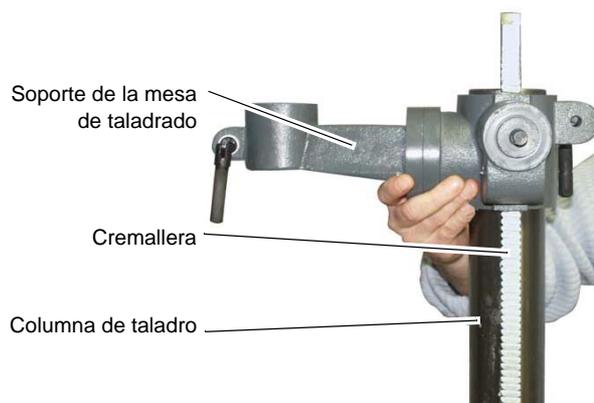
Montaje soporte de la mesa de taladrado (B20)
